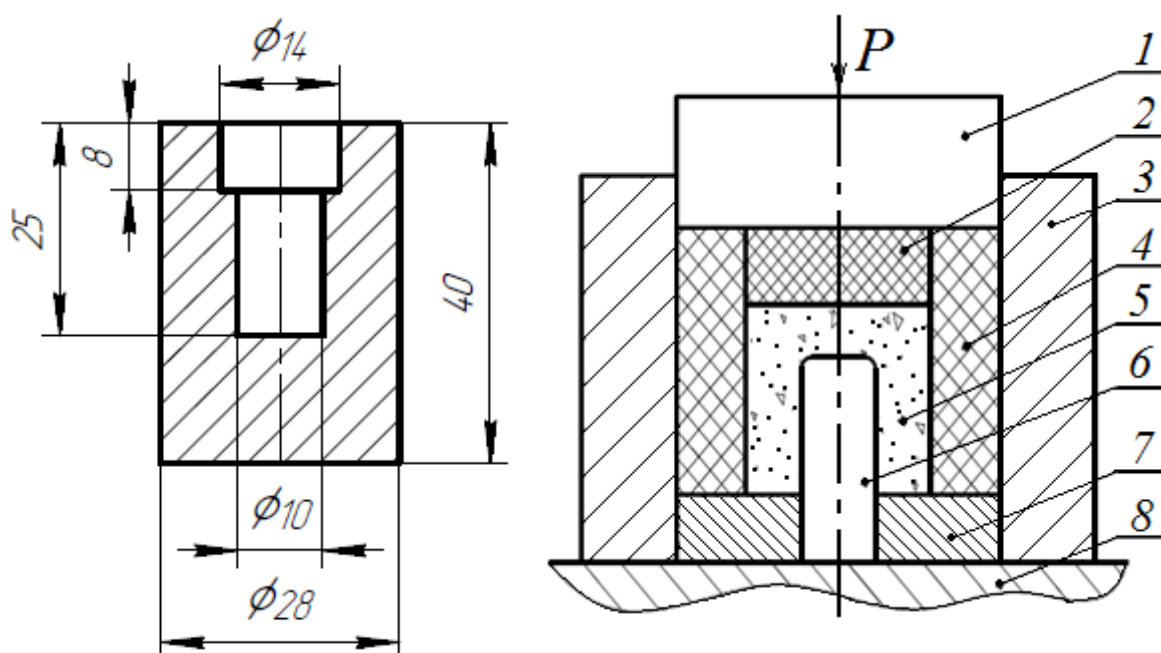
а) - эскиз вкладыша; б)- принципиальная схема ЭСП профилированной заготовки: 1 - пуансон; 2 – эластичная вставка; 3-контейнер; 4 - эластичная втулка; 5 – порошок; 6 – оправка; 7 – опора; 8 – плита
